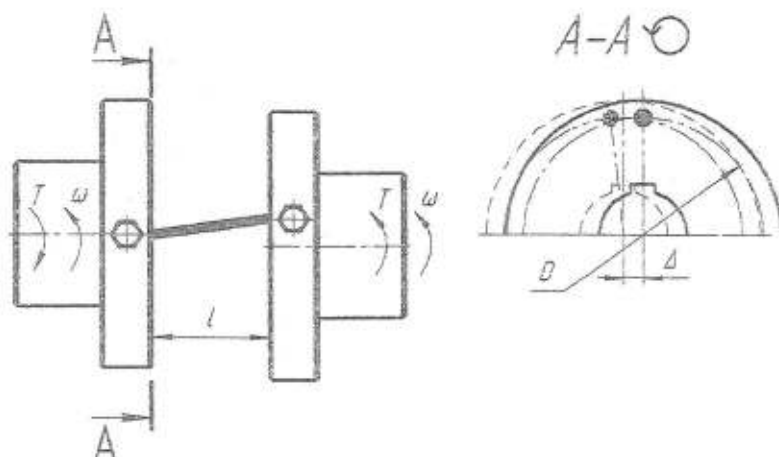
Схема муфти з осью паралельною установкою канатів прямолінійної форми
